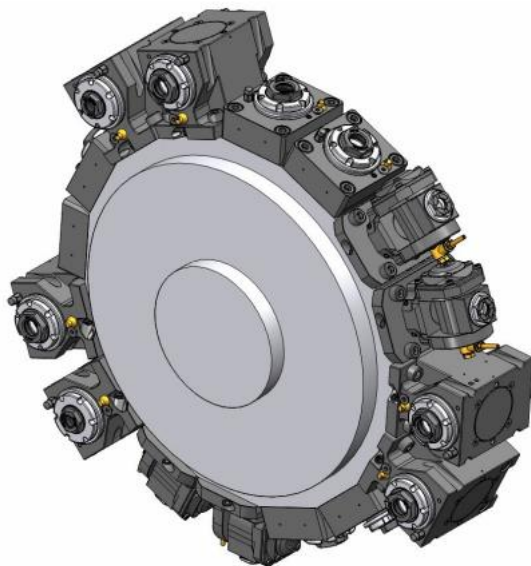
Револьверная головка станка Okuma LT2000EX MY
